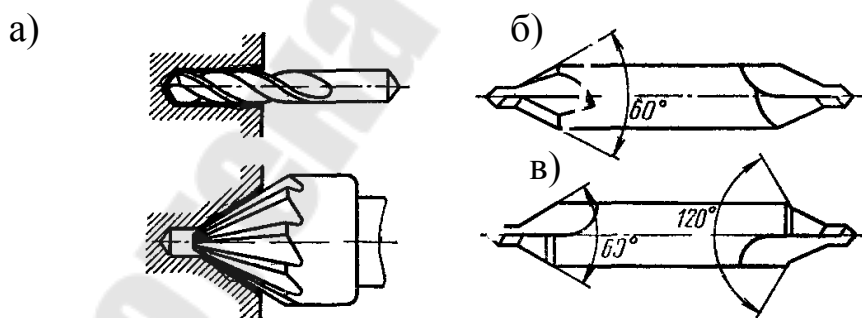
Схема центрования (а) и центровочные сверла (б, в)
